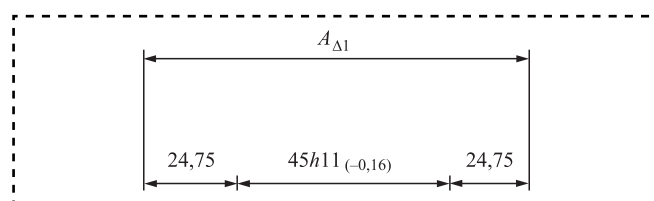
Размерная цепь подшипник—колесо—подшипник выходного вала редуктора
